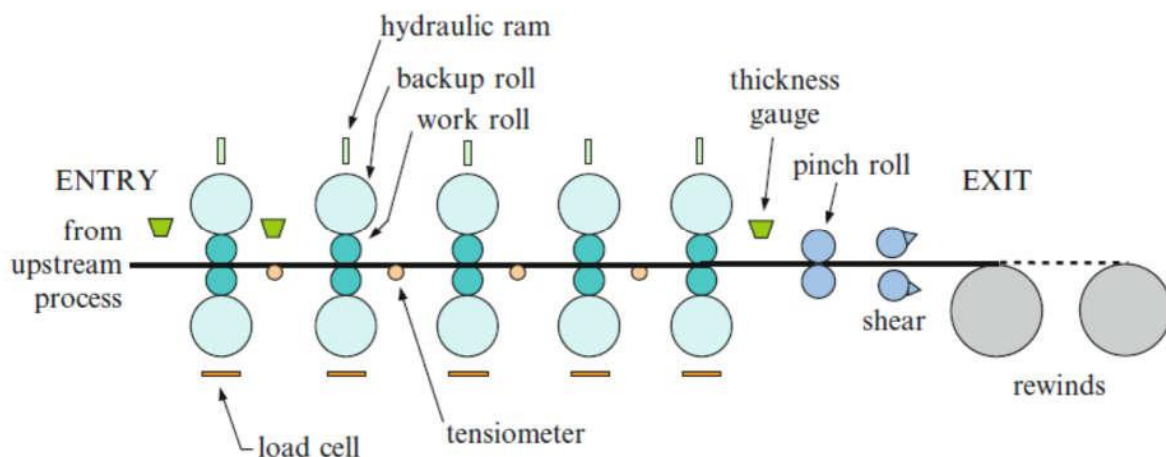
moulin froid tandem de Cinq-support, configuration continue
